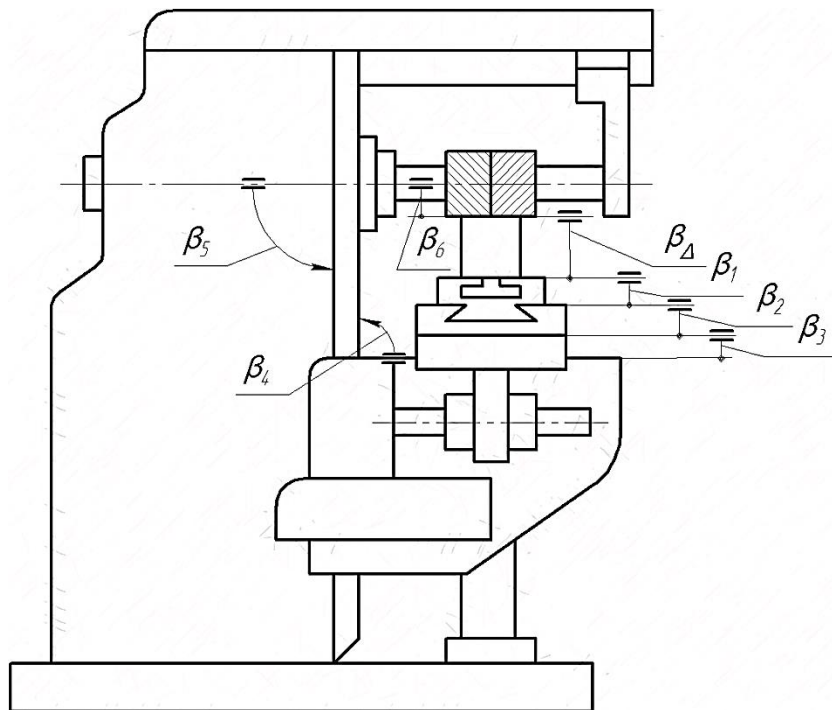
Схема технологічного розмірного ланцюга фрезерного верстата
